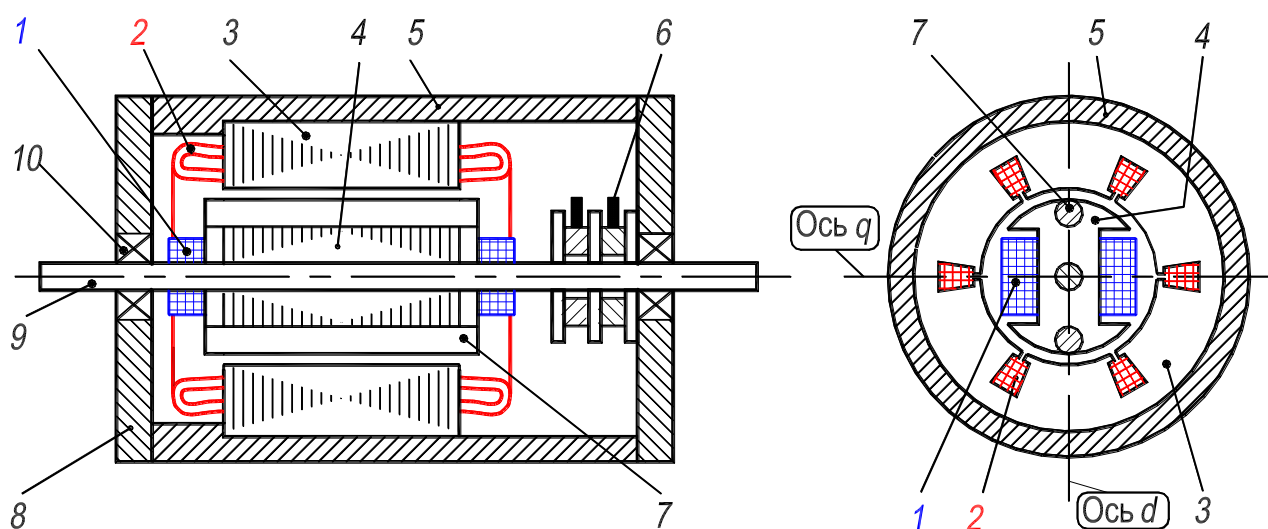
Конструктивная схема контактного сельсина: 1 – обмотка возбуждения; 2 – трехфазная синхронизирующая обмотка; 3 – сердечник статора; 4 – сердечник ротора; 5 – корпус; 6 – контактное кольцо со щеткой; 7 – демпферная обмотка; 8 – крышка; 9 – вал; 10 – подшипник; ось d – продольная; ось q – поперечная
